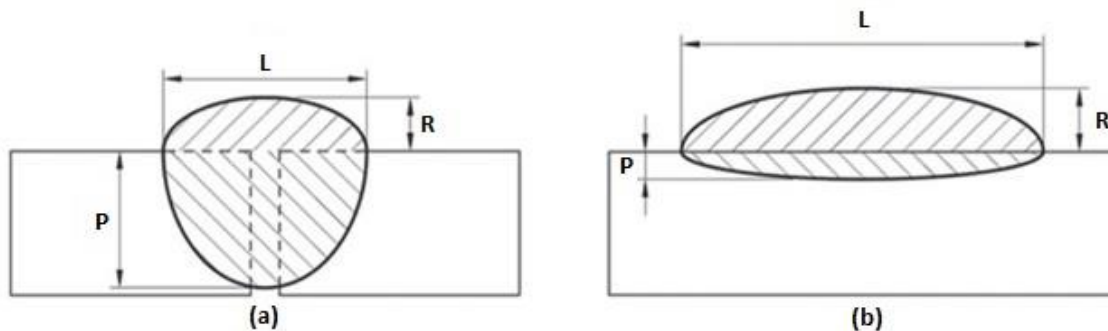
Perfil geométrico desejado na (a) união de junta soldada e (b) soldadura de revestimento [32]
